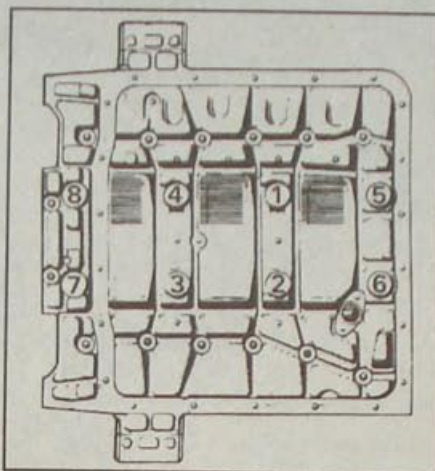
Последовательность затягивания гаек крепления опоры коренных подшипников
